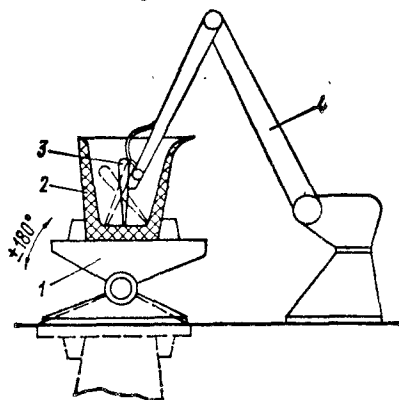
Роботизированный комплекс для чистки и выбивки футеровки разливочных ковшей:
